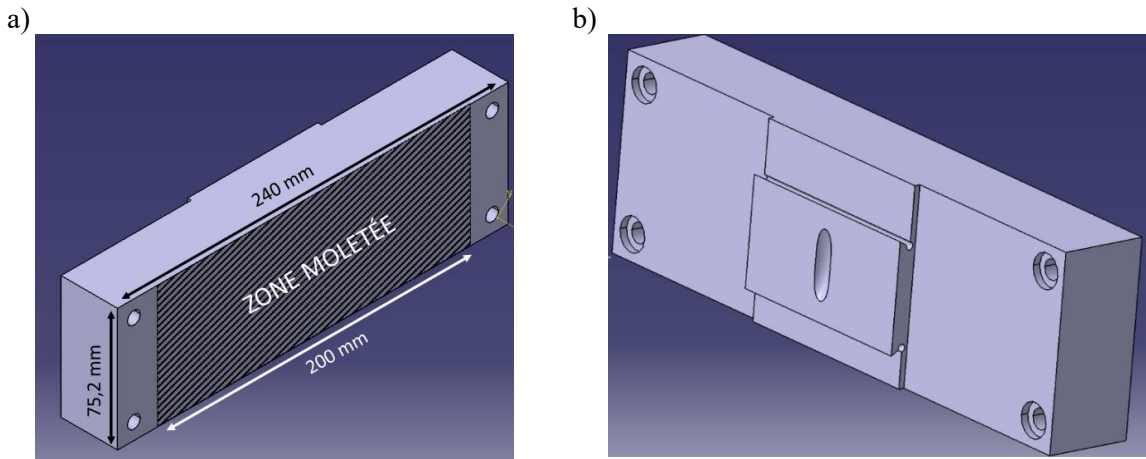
Plaquette de mors usinée adaptée aux dimensions de l'éprouvette, vue de face (a) et arrière (b).
